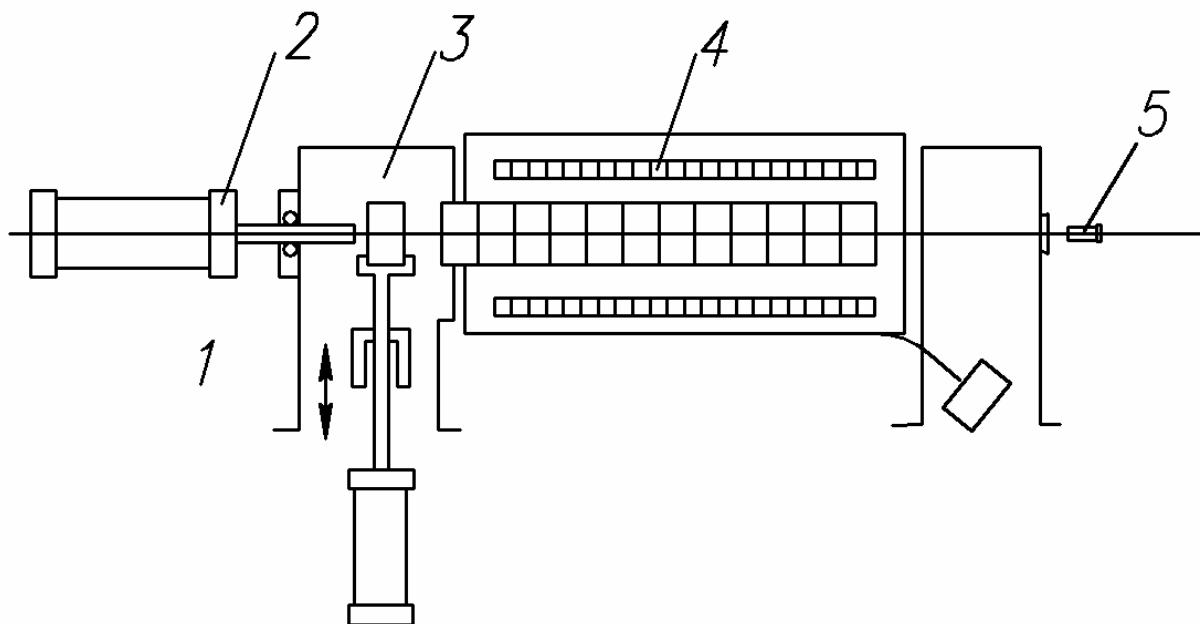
Нагреватель для малоокислительного нагрева: 1 – подъемник заготовок; 2 – толкатель; 3 – камера; 4 – индуктор; 5 – пирометр
